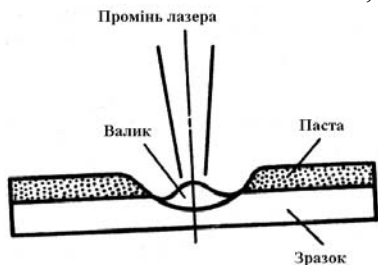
Схема лазерного легування або наплавлення з нанесенням порошкової паст на поверхню
